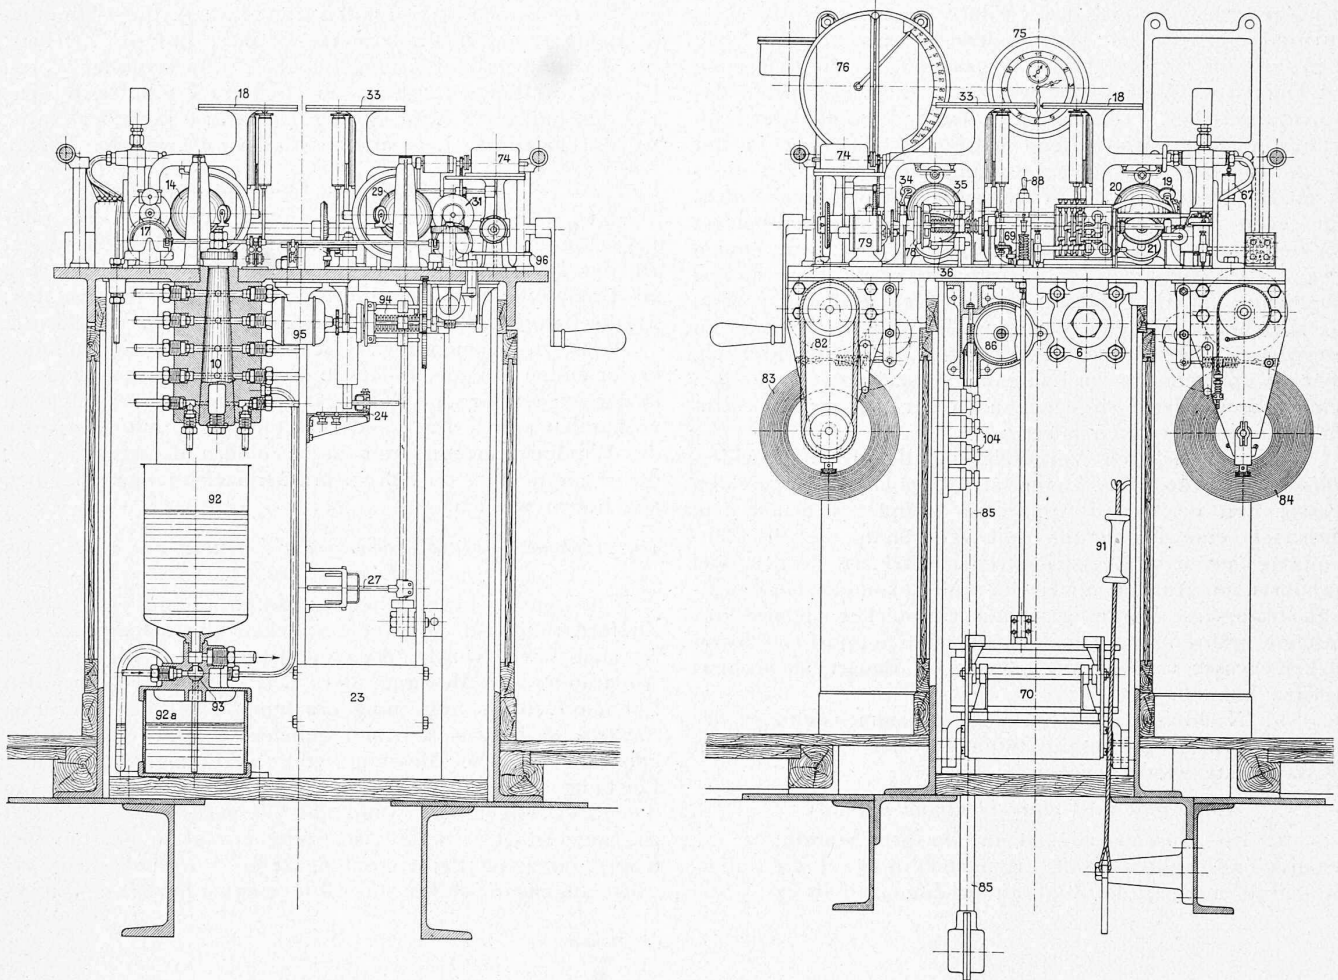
Querschnitt von „Vorn“ gesehen. — Masstab 1:12,5. — Abb. 31. Ansicht vom Beobachter-Standpunkt aus.
